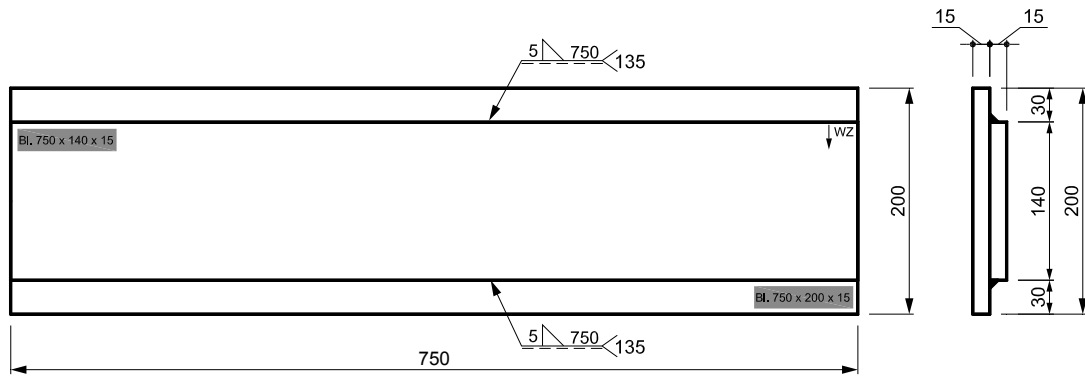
Versuchskörper - Schweißnahtausführung
